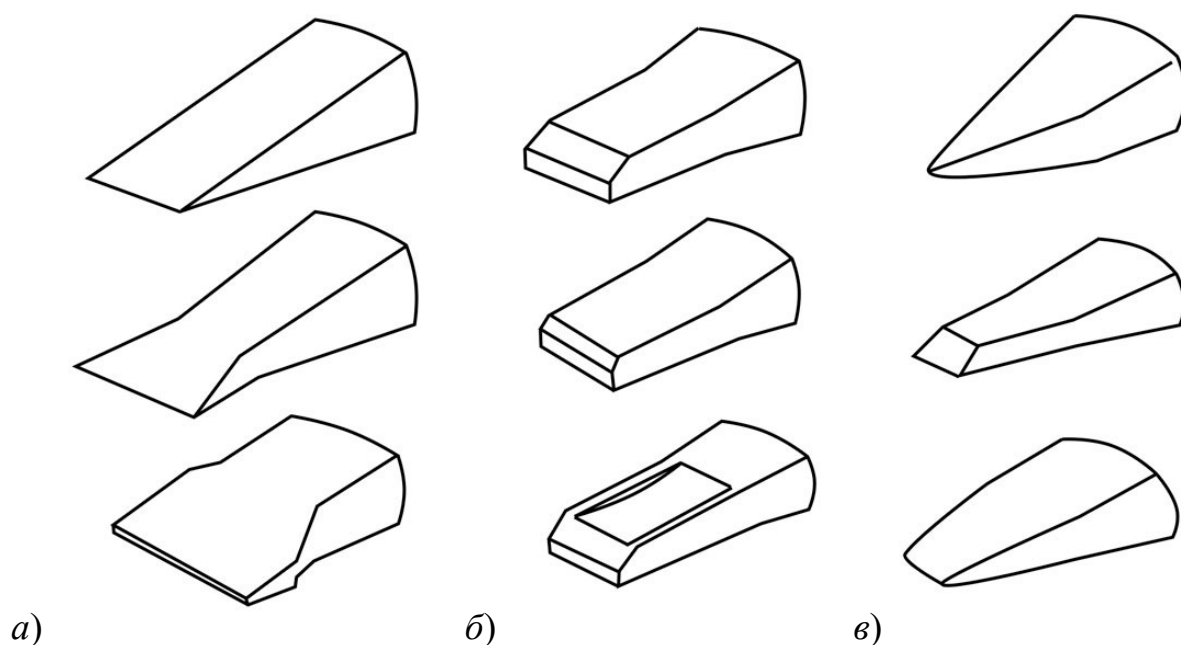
Строение режущей части зубьев (коронки) ковша экскаватора [72]
